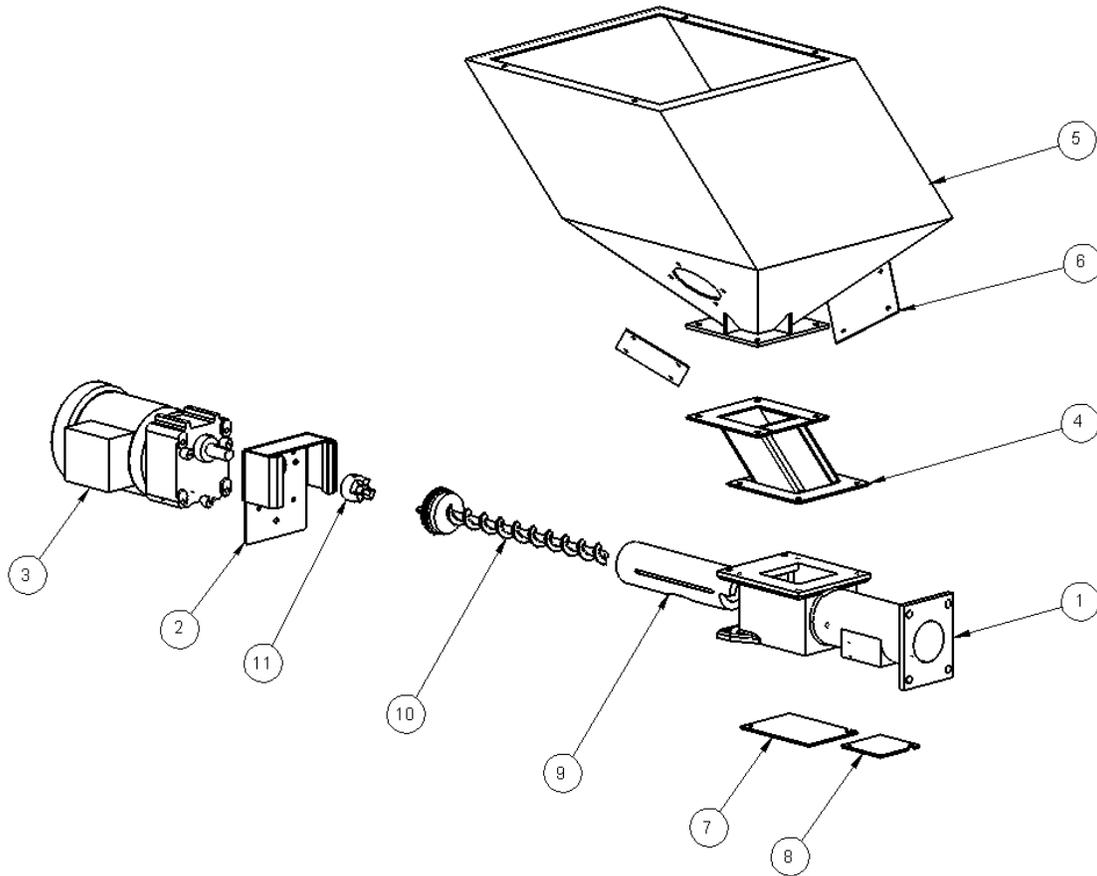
Lista de partes del ensamble típico de la tolva de alimentador aditivo
